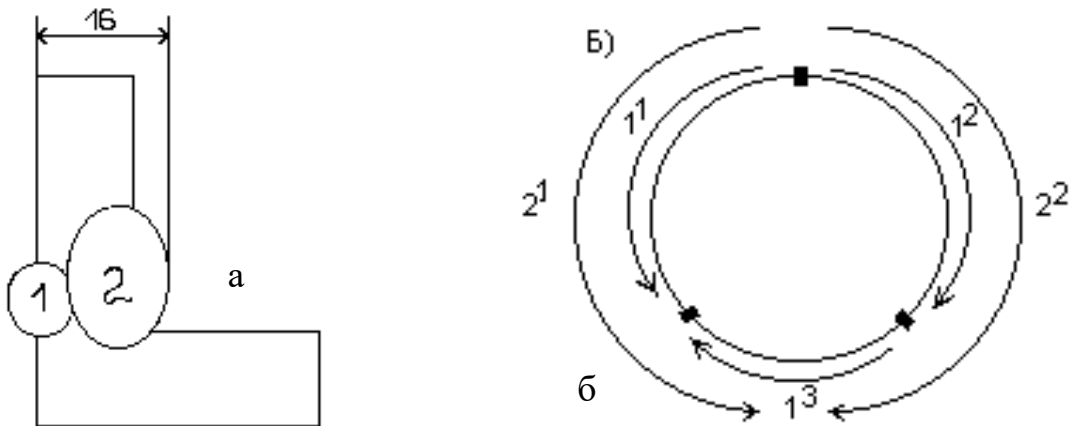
Схема заповнення зварного шва: а – по січенню; б – по довжині
